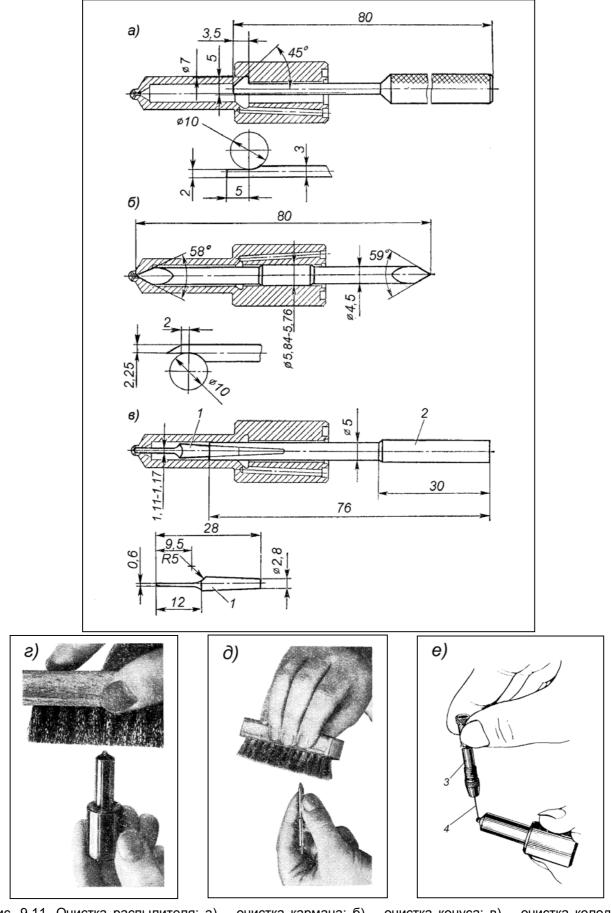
Очистка распылителя: а) — очистка кармана; б) — очистка конуса; в) — очистка колодца (латунными скребками): 1 — скребок; 2 — державка; r) — очистка носика корпуса; д) — очистка конуса иглы (щеткой из латунной проволоки); е) — очистка отверстий корпуса: 3 — державка, 4 — стальная проволока (или сверло) по диаметру отверстия.
